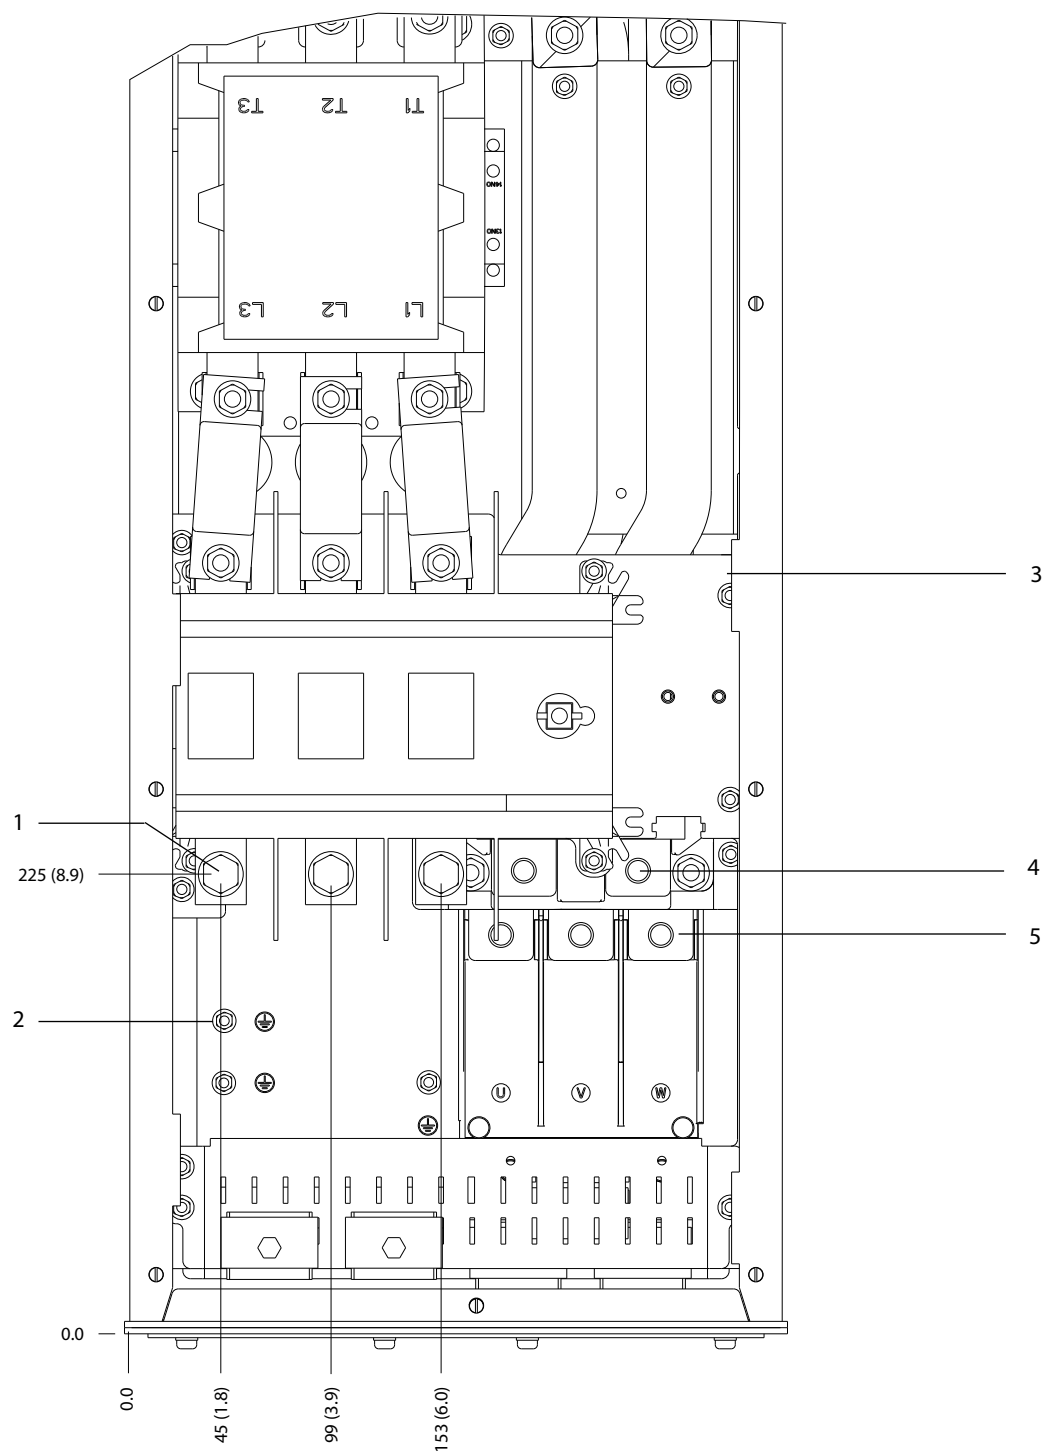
Dimensões do terminal do D6h com opcional de contator (vista frontal)
